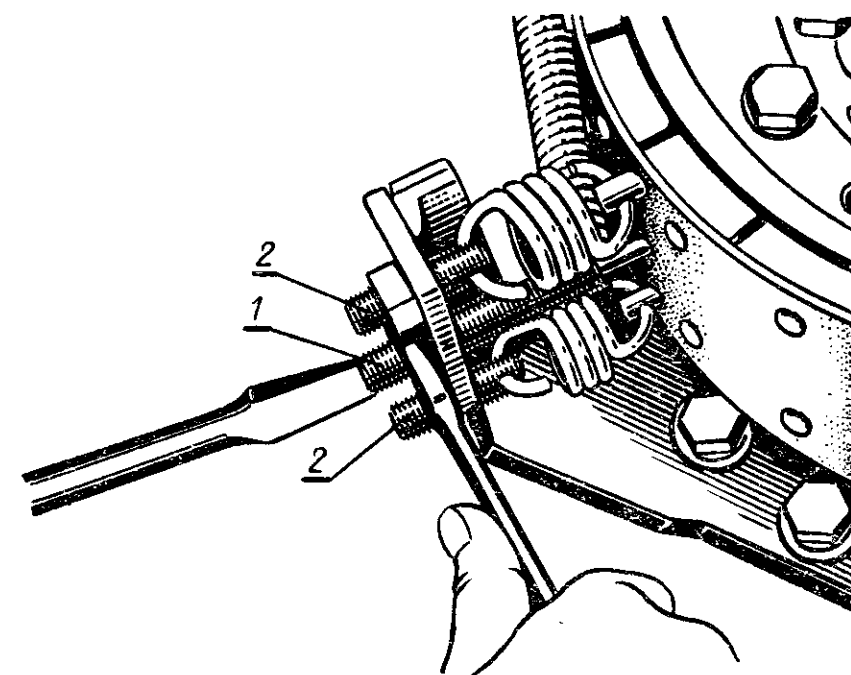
Регулировка зазора между лентой и барабаном стояночного тормоза:
